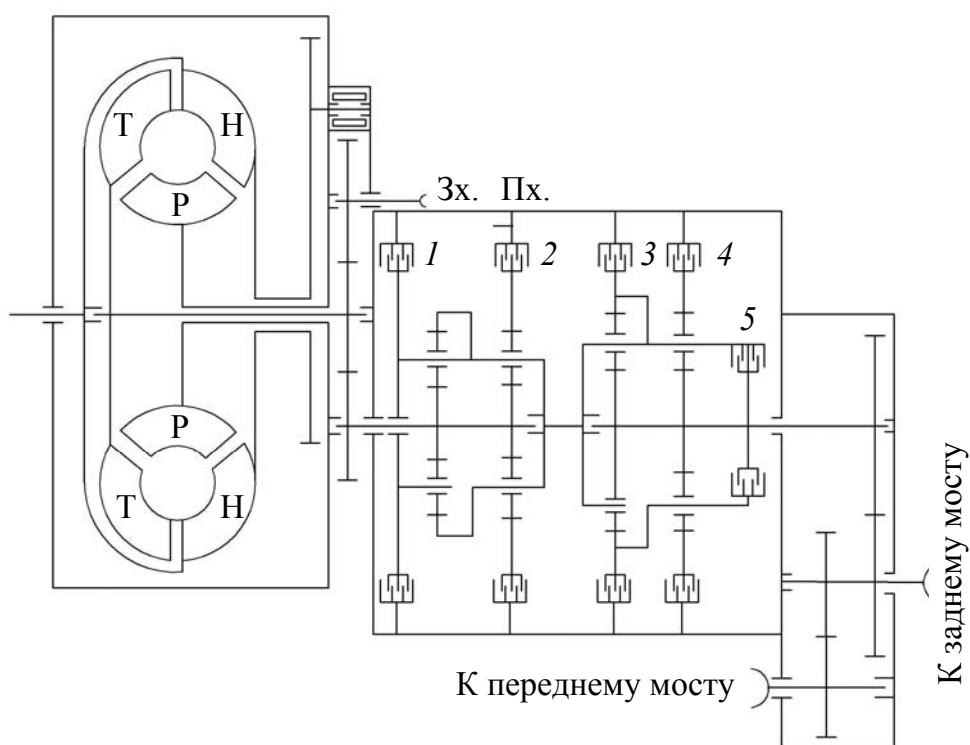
Схема ГМП с планетарной трехскоростной коробкой передач:
